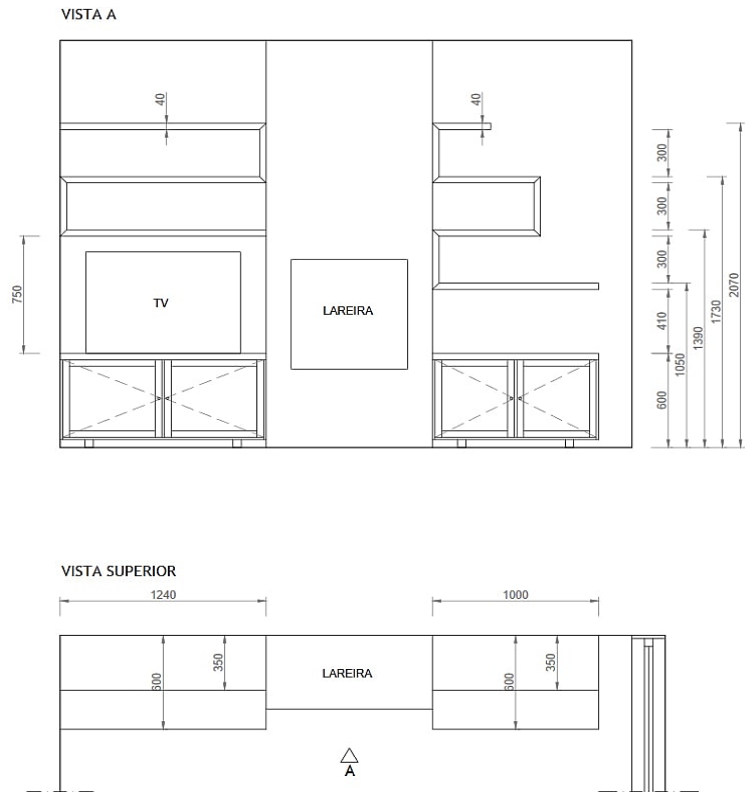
Desenho técnico. Cotagem geral dos equipamentos.
